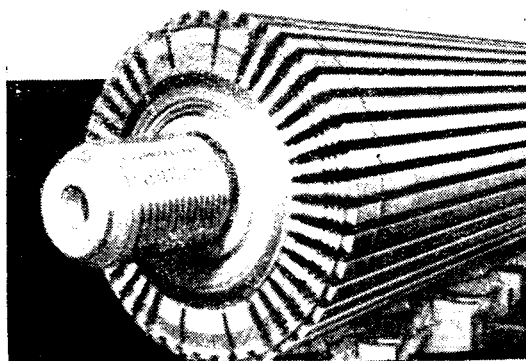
Общий вид ротора генератора 187,5 тыс. кВа без обмотки со снятым концом вала.
